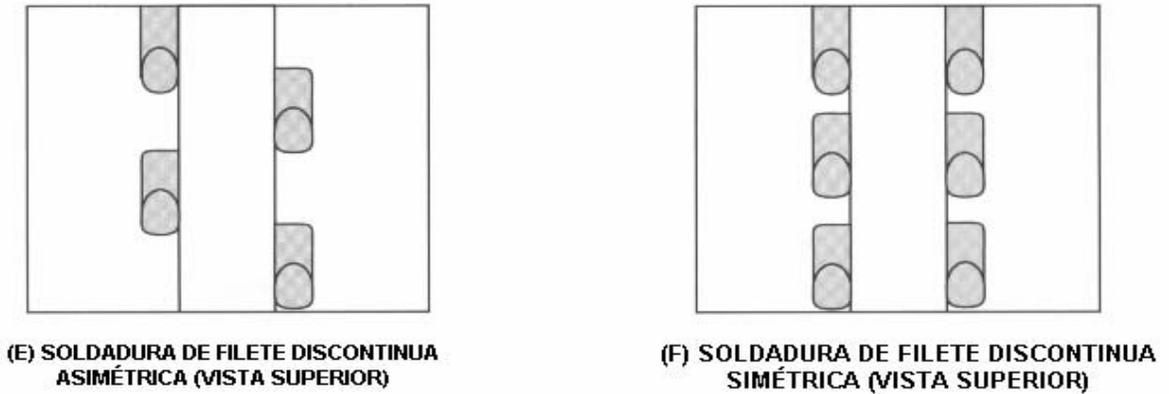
(continuación) – Aplicaciones de la soldadura de filete
